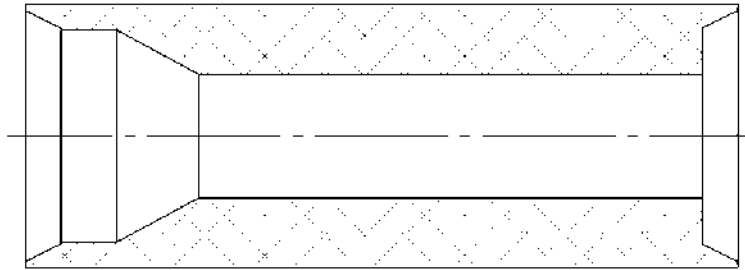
Схема еластичної оболонки з поліуретану марки СКУ-7Л для виготовлення сопла піскоструменевої машини промислового призначення.
